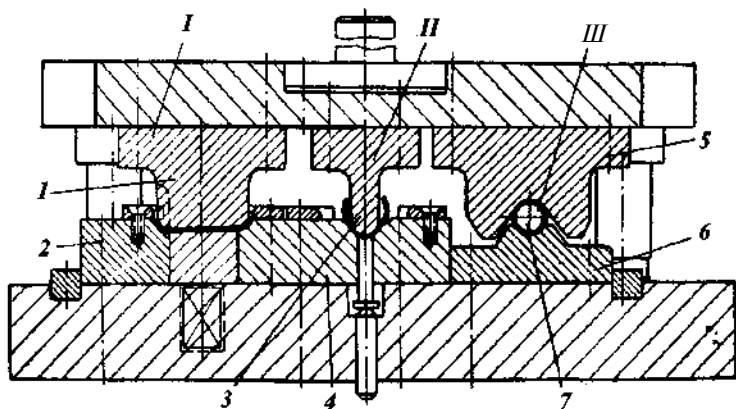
Штамп последовательного действия с ручной загрузкой штучных заготовок:
